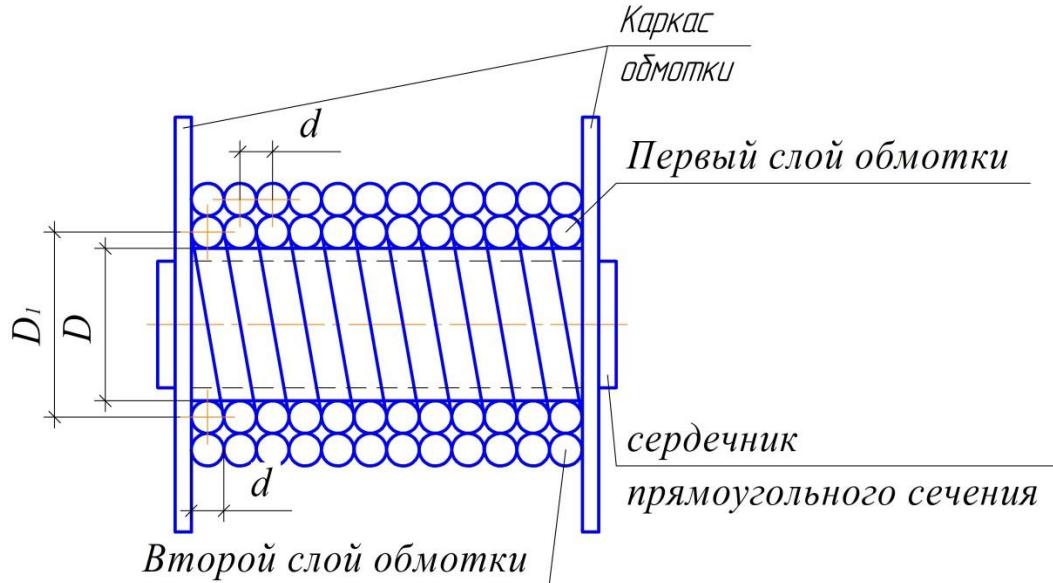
Внешний вид рассматриваемой обмотки электромагнитного устройства
